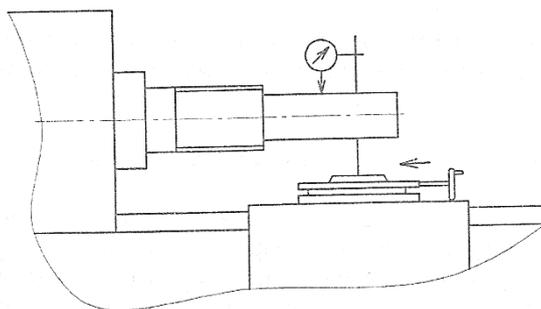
Схема установки индикатора для проверки параллельности направления перемещения салазок суппорта оси шпинделя
